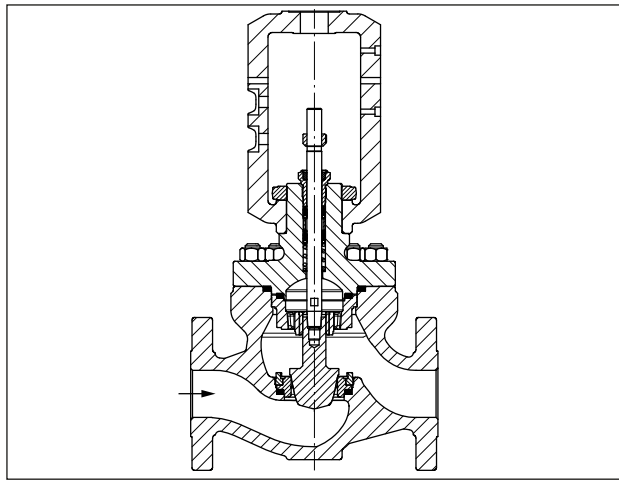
Durchgangsventil Typ 251GR mit geschraubtem Sitz
